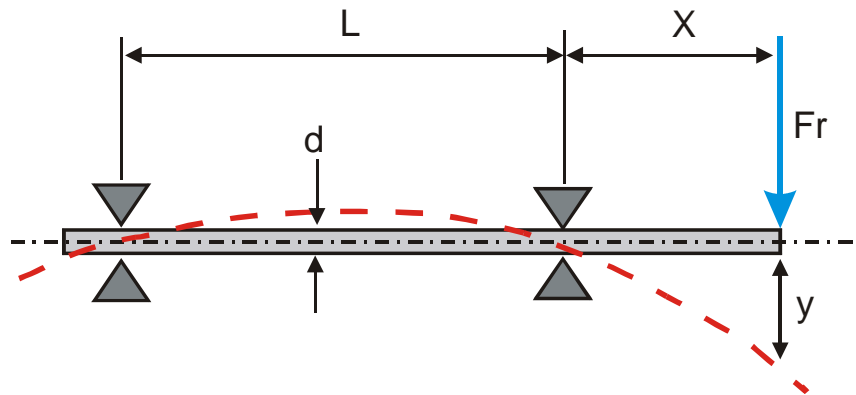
Prinzip­skizze einer Spindel mit einer 2-Punkt-Lagerung [8]
